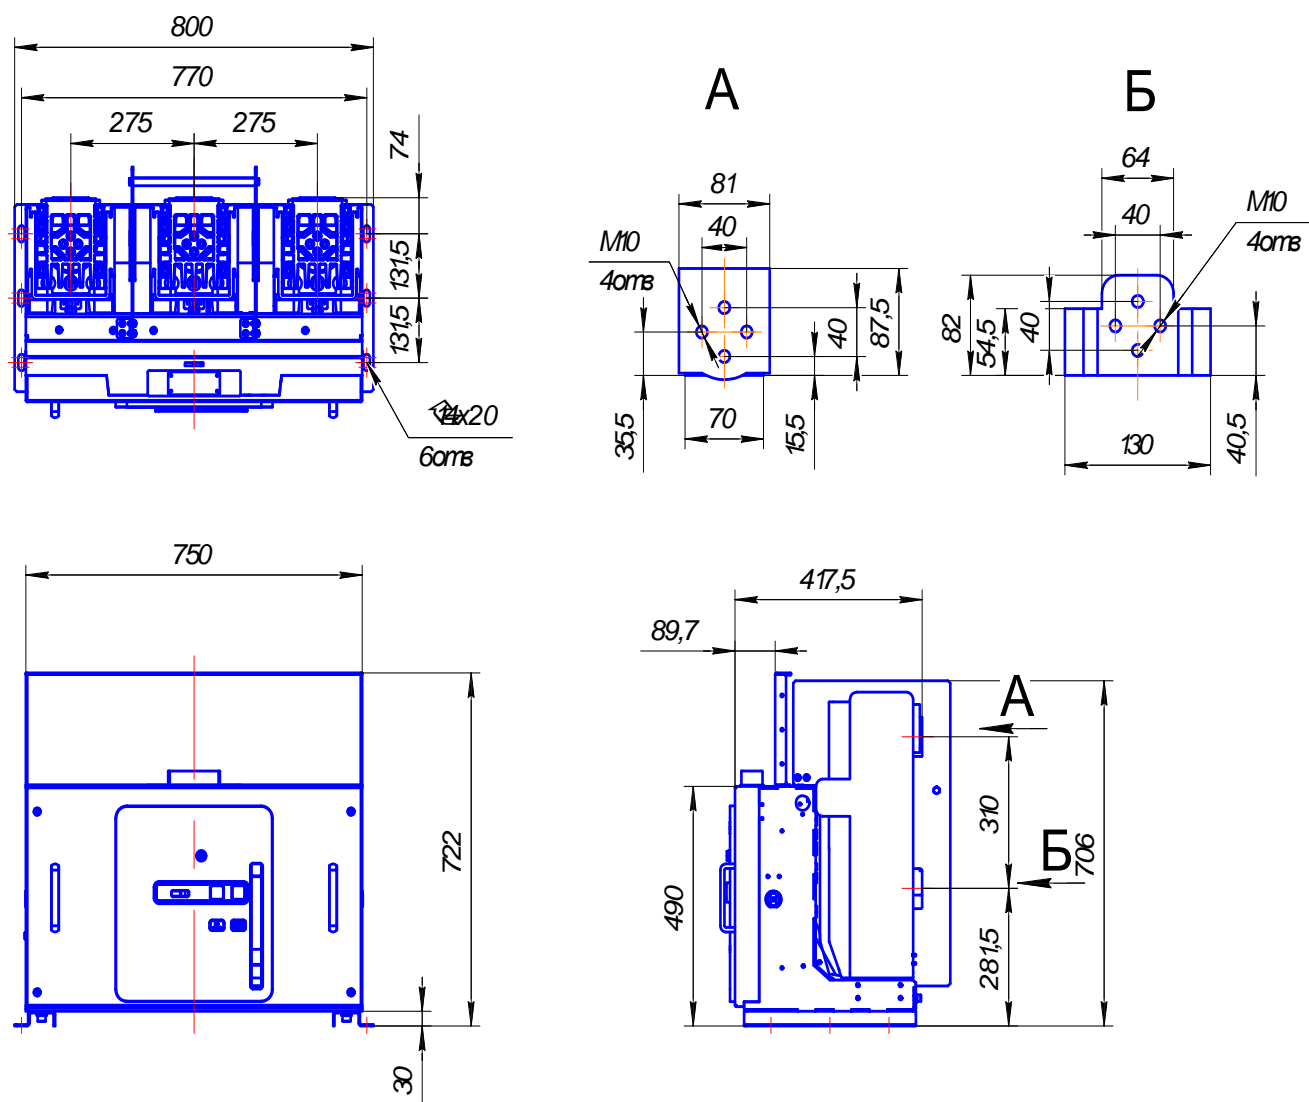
Габаритный чертеж выключателя вакуумного типа ВВ-ЧЭАЗ-2-С-10-40/4000У3.
